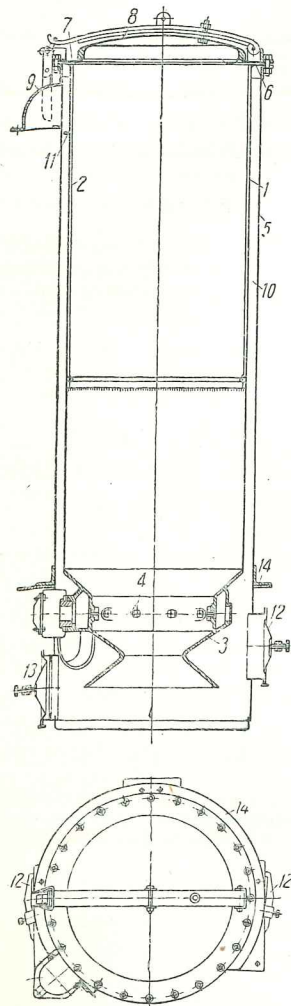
Схема газогенератора установки ЗИС для автомобиля ЗИС-21
